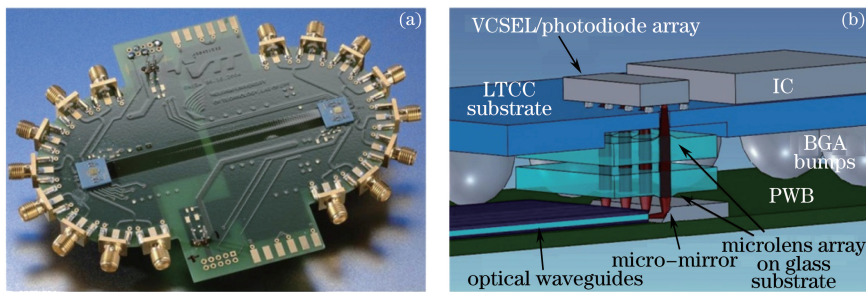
VTT 实验光电互联 PCB 板。(a) 实物图; (b) 组件结构及光电耦合示意图
